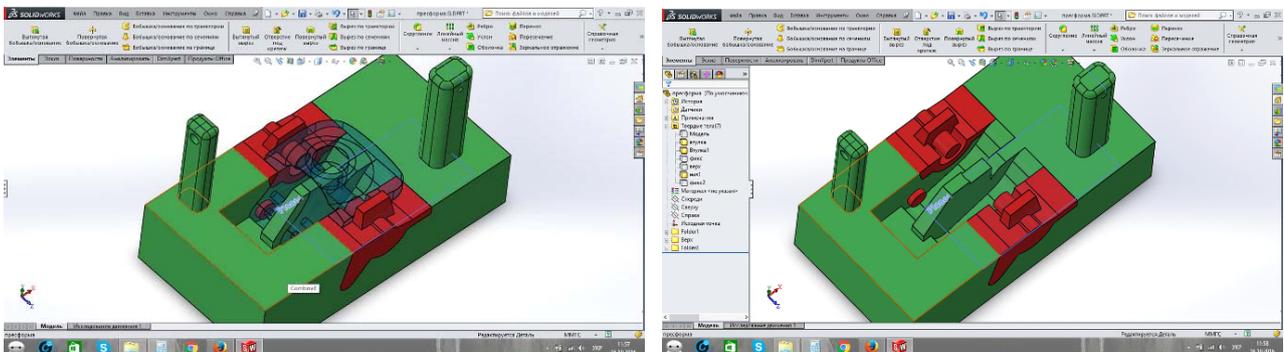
3D-пресс-форма литья восков для деталей протеза
